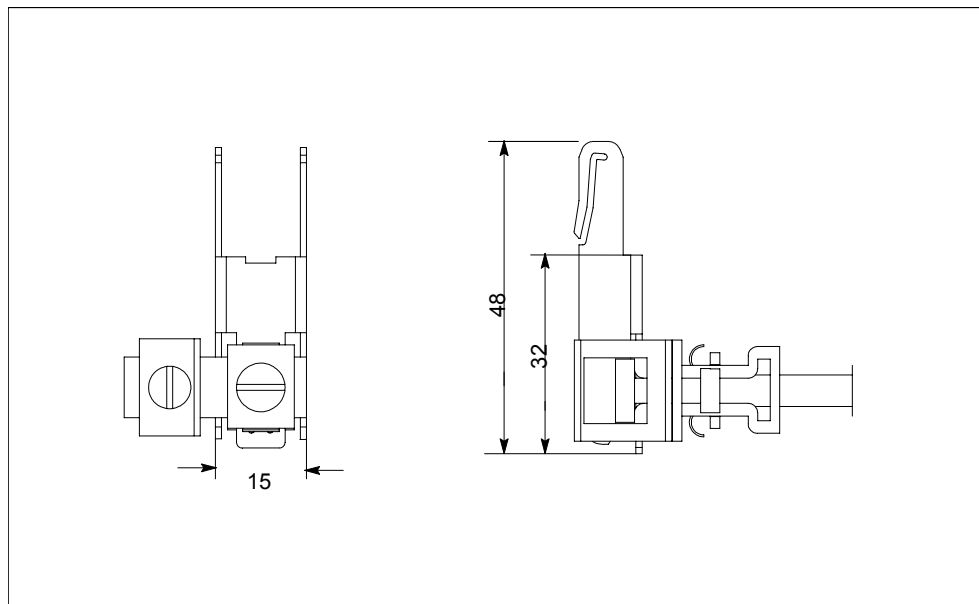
Габаритный чертеж контакта-опоры для экрана
